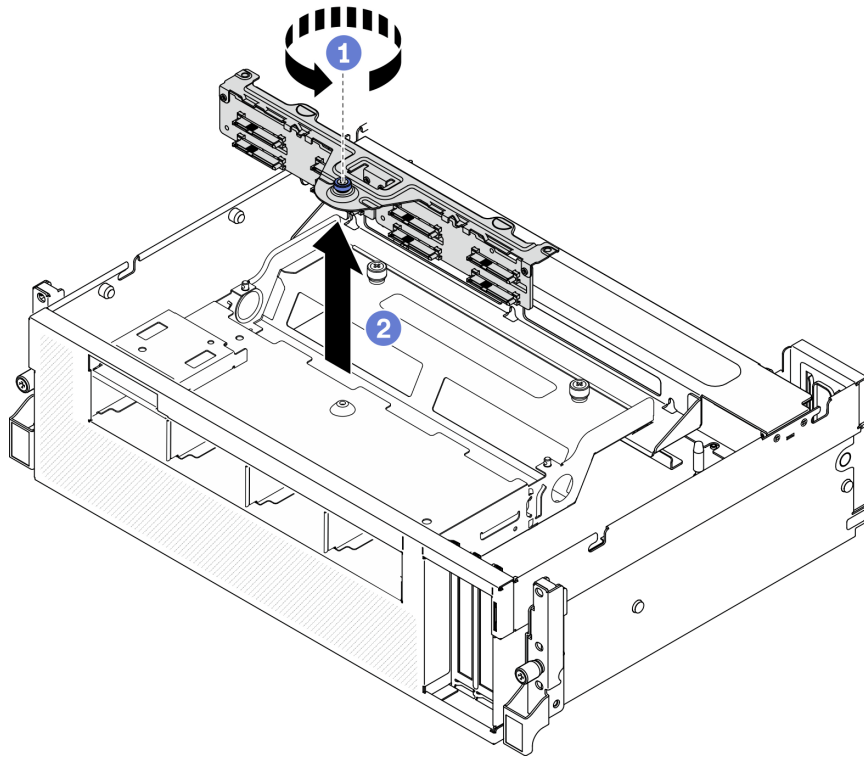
Entfernen des Rückwandplattenmoduls für 2,5-Zoll-Laufwerke
